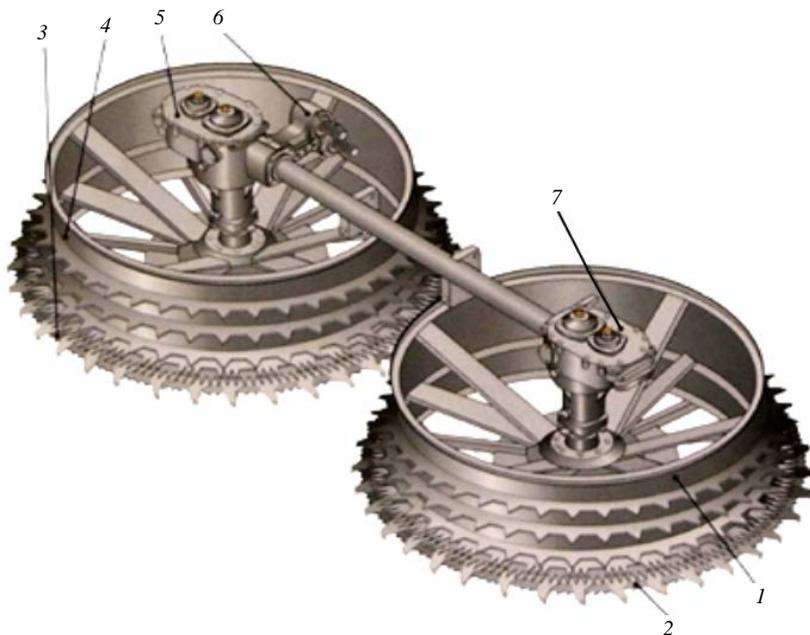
Блок барабанов с угловым приводом: *1* – барабан левый; *2* – режущий аппарат левый; *3* – режущий аппарат правый; *4* – барабан правый; *5* – угловой редуктор правый; *6* – цилиндрический редуктор; *7* – угловой редуктор левый
